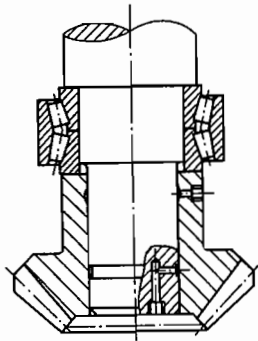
轴与轴承、齿轮的过盈连接及拆开时用的注油螺口管道
